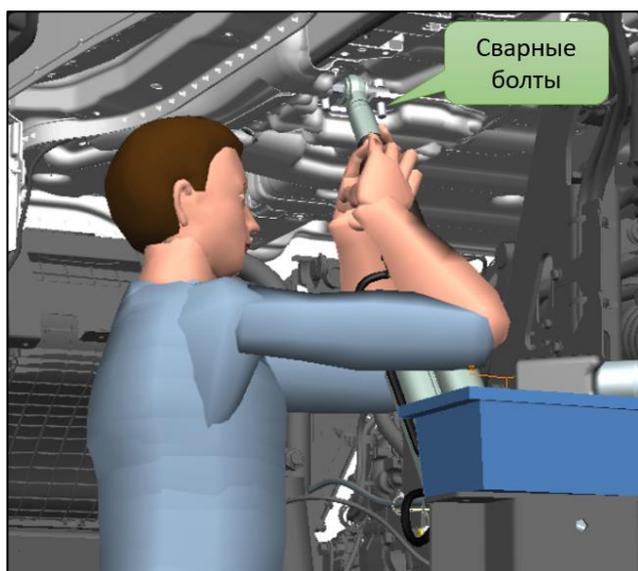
Процесс установки гидроцилиндра в сборе с болтами
